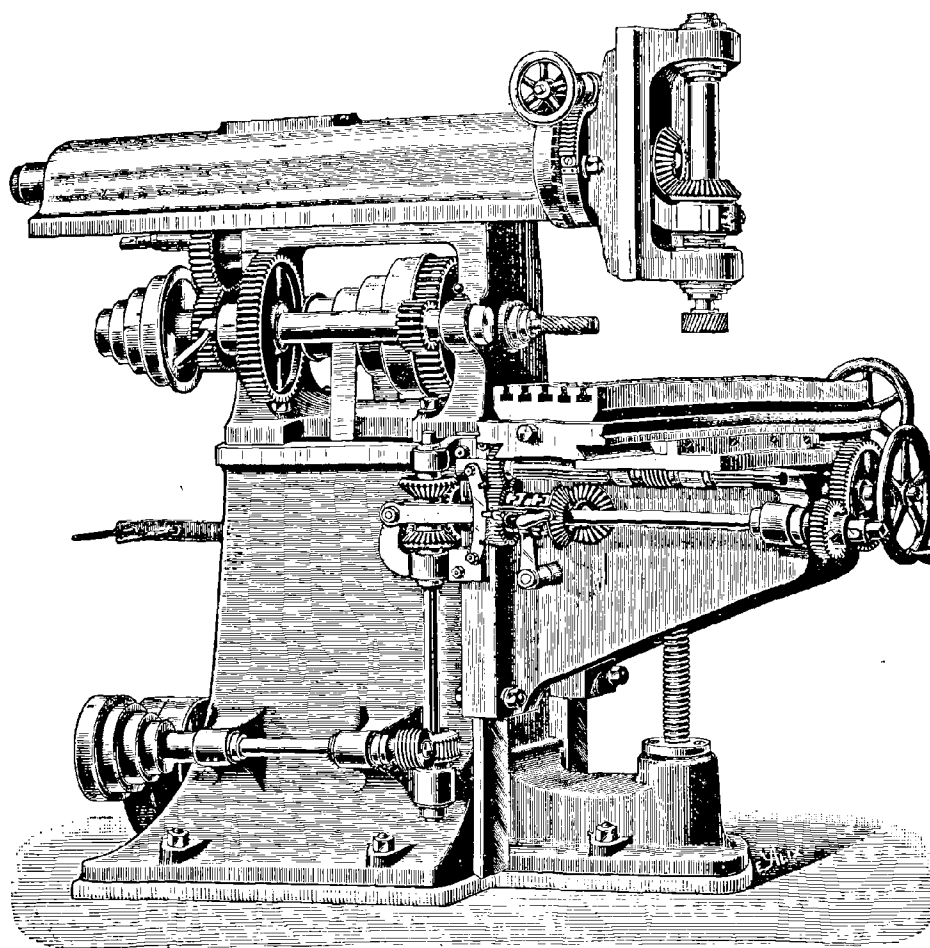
Machine à fraiser horizontalement, verticalement et sous une inclinaison quelconque.
